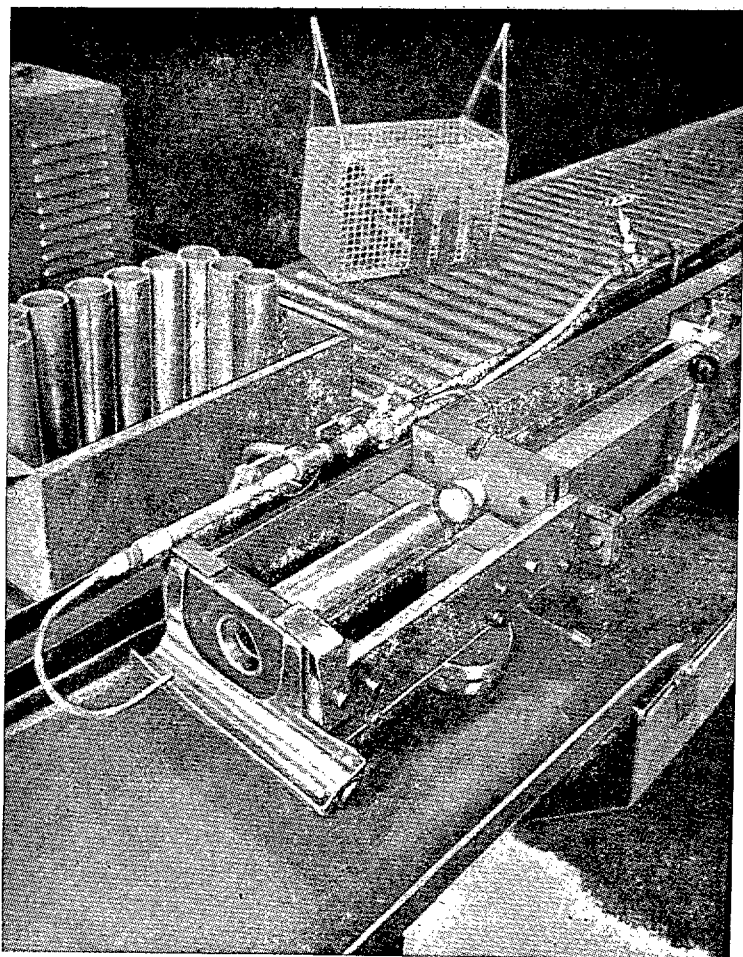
ª—Brochadora hidráulica de bola de carburo de tungsteno, para pulimentar la superficie interior del cuerpo del motor-cohete.
